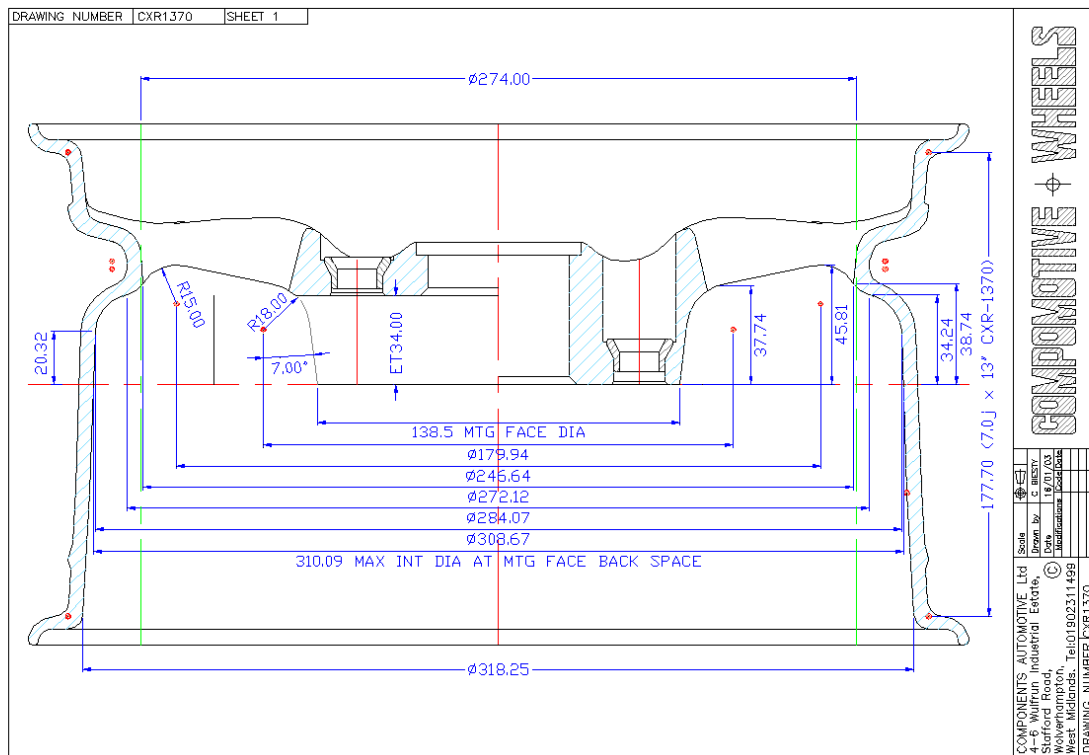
Dimensões da jante escolhida. Desenho técnico cortesia da Compomotive [16]
